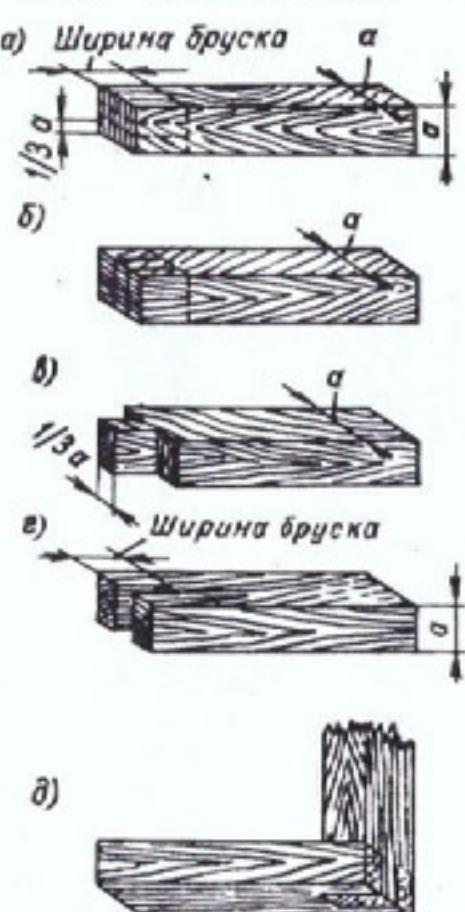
Последовательность операций при изготовлении шипов и проушин: а — разметка; б — пропил; в — выделка шипа; г — выделка гнезда; д — сборка брусков.
